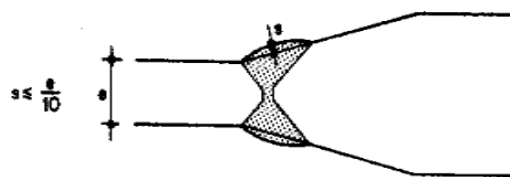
B Sobre espesor  $s$  de una soldadura a tope
